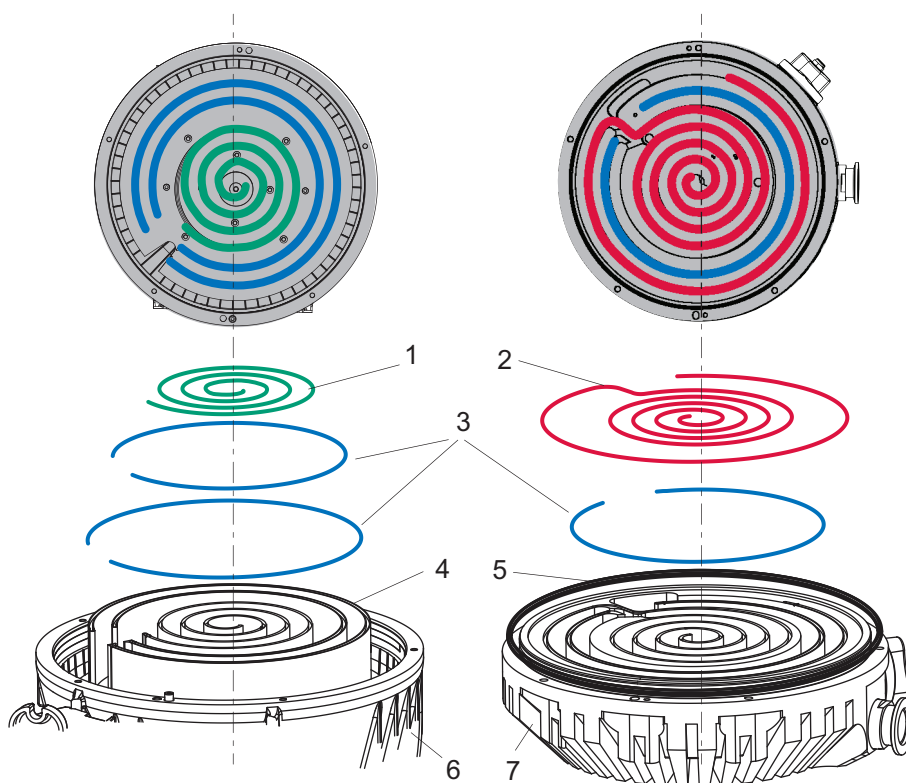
Remplacement des joints d'extrémité sur la pompe scroll
